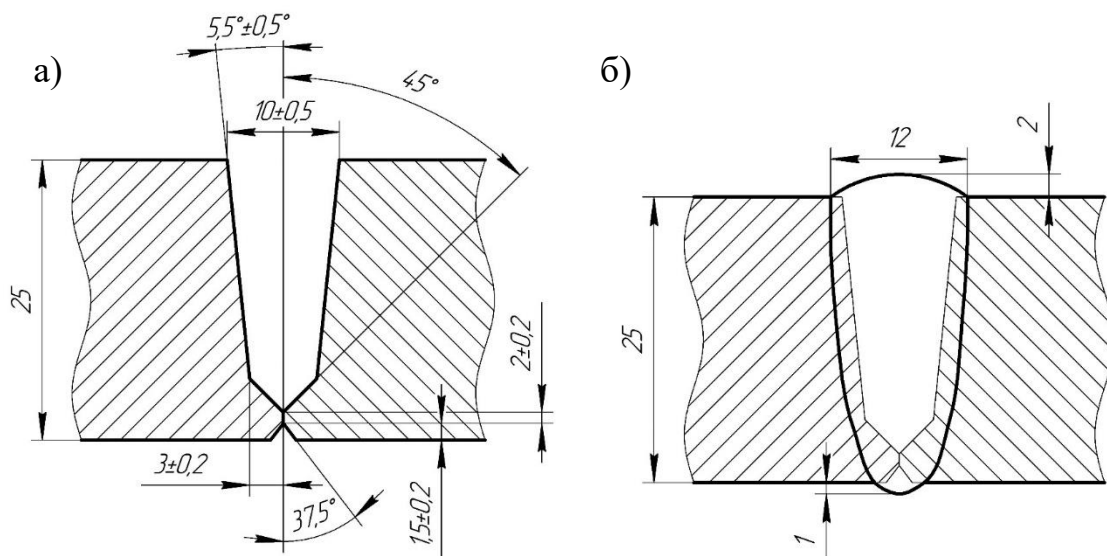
CRC-Evans: а) разделка кромок; б) поперечное сечение сварного шва.
